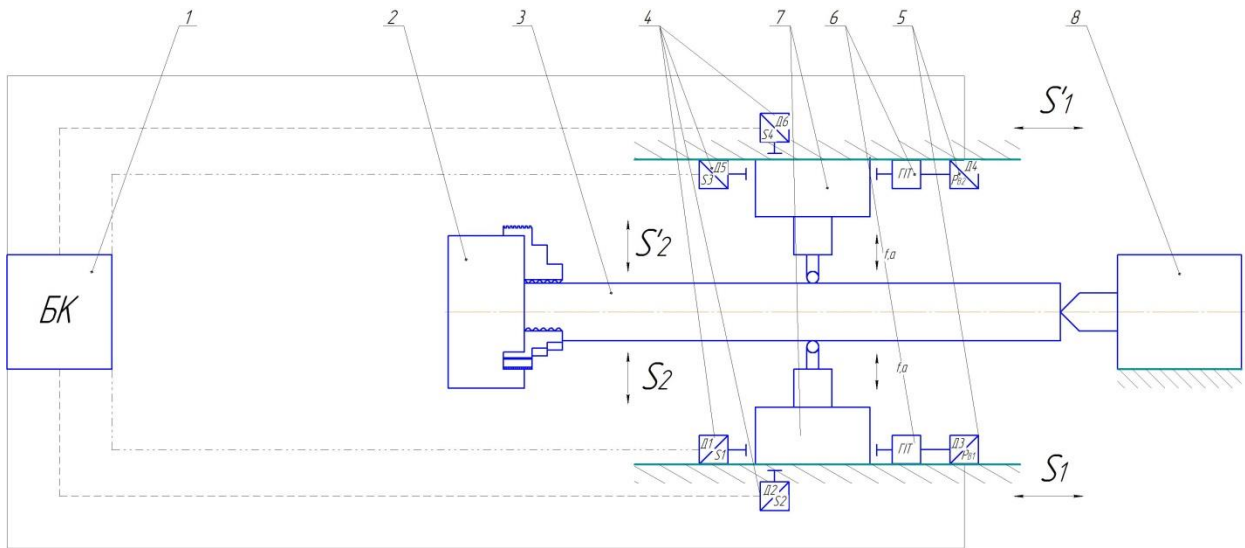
Принципова схема пристосування для деформаційного зміцнення деталей машин:
